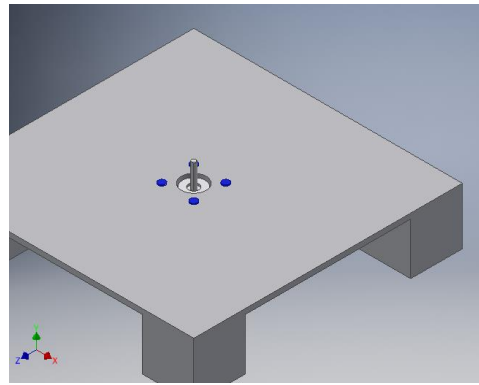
MONTAJE DE MOTOR EN LA BASE
